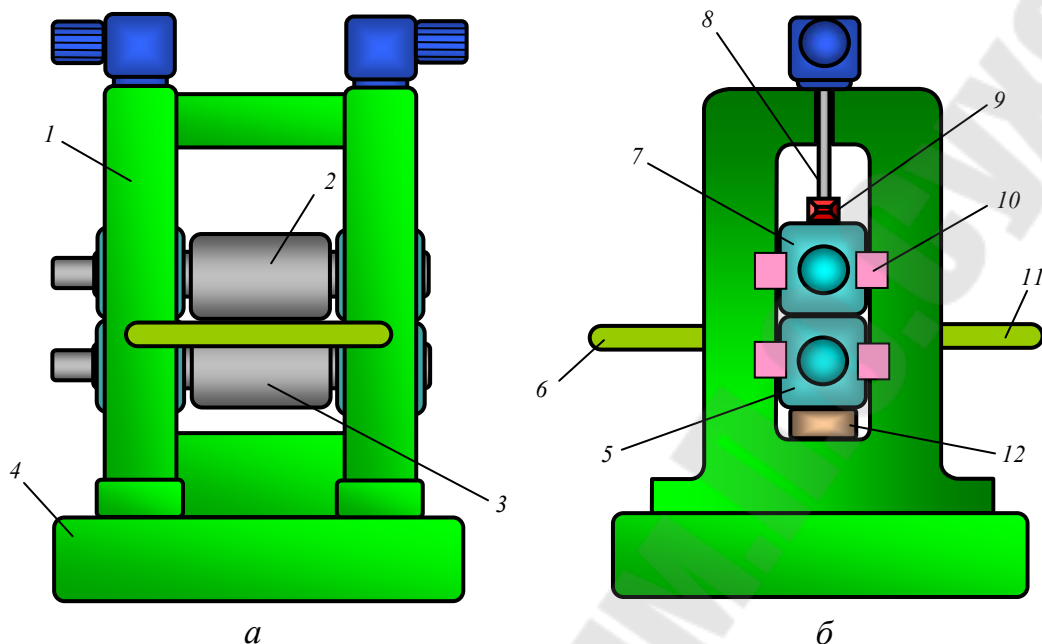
Прокатная клеть: *а* — вид спереди; *б* — вид сбоку; 1 — станина; 2, 3 — верхний и нижний рабочие валки; 4 — плитовина; 5, 7 — нижняя и верхняя подушки; 6, 11 — входной и выходной столы с линейками; 8 — нажимное устройство; 9 — предохранительное устройство; 10 — устройство осевой установки и фиксации валков; 12 — устройство уравнивания валков.
